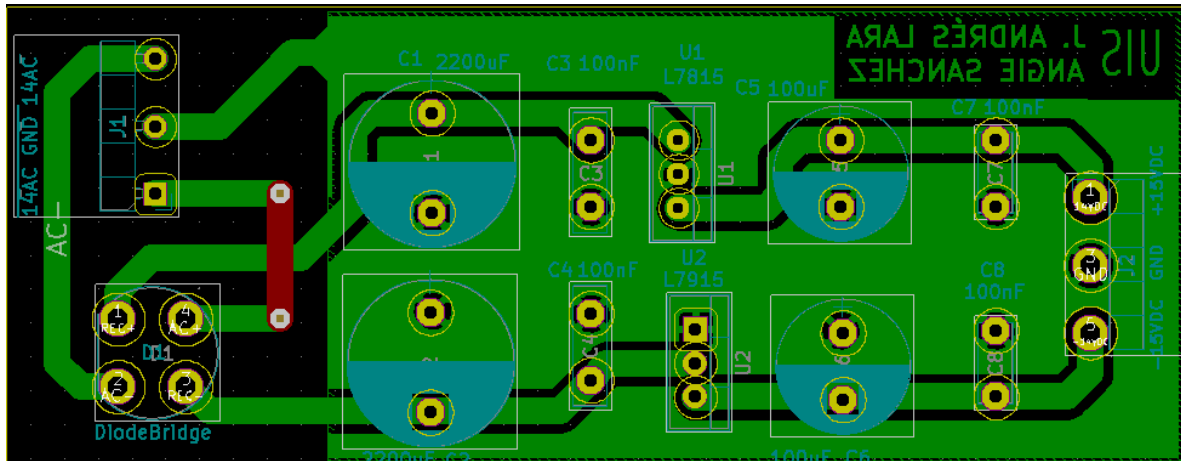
Circuito PCB de la fuente de ± 15 [V] D.C. Fuente Autores.
